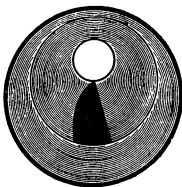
Неправильная сверловка ствола — односторонний выхват металла перед патронником
